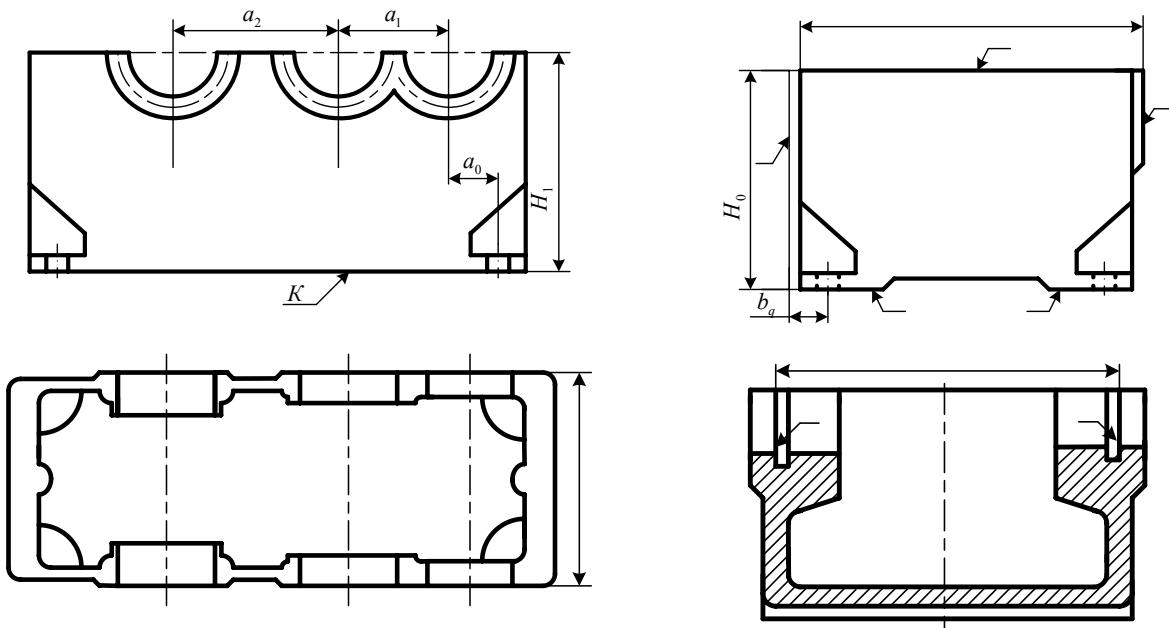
Корпуси редукторів і коробок швидкостей
